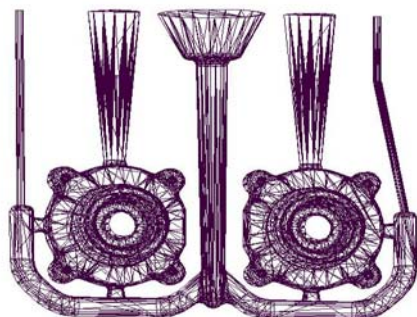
Отливка «Крышка» с литниковопитывающей системой: сеточная 3D модель (Solid Cast, [4])
